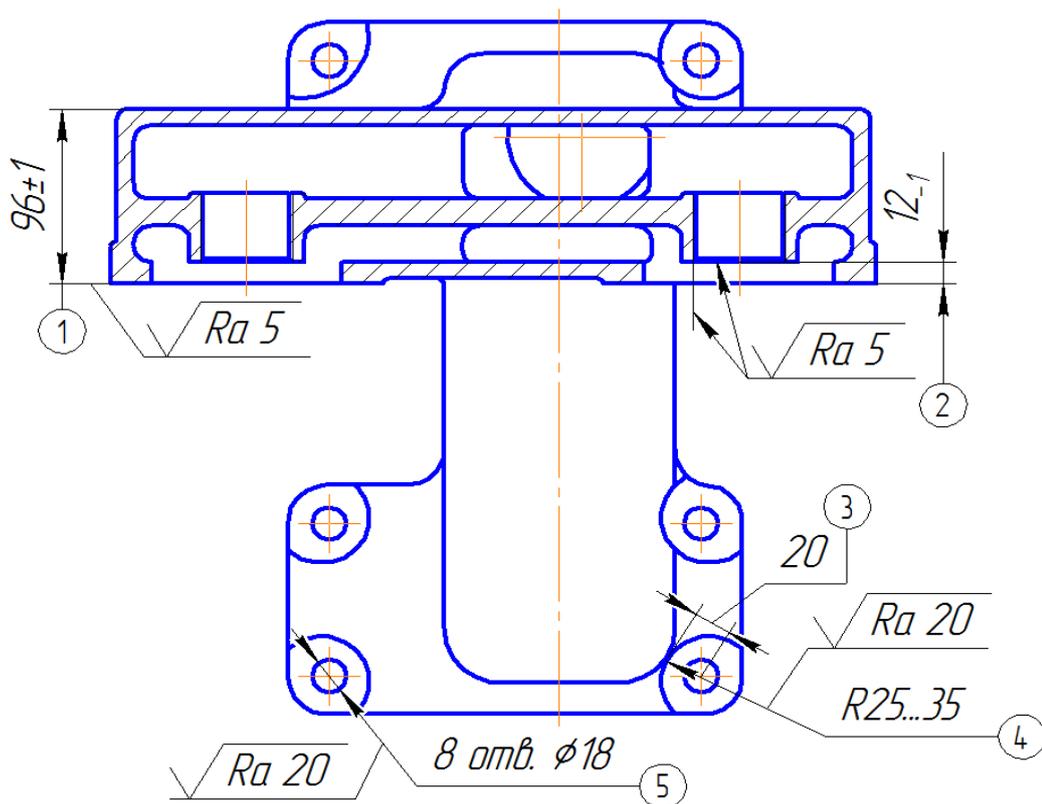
Эскиз детали «Корпус масляного фильтра»
